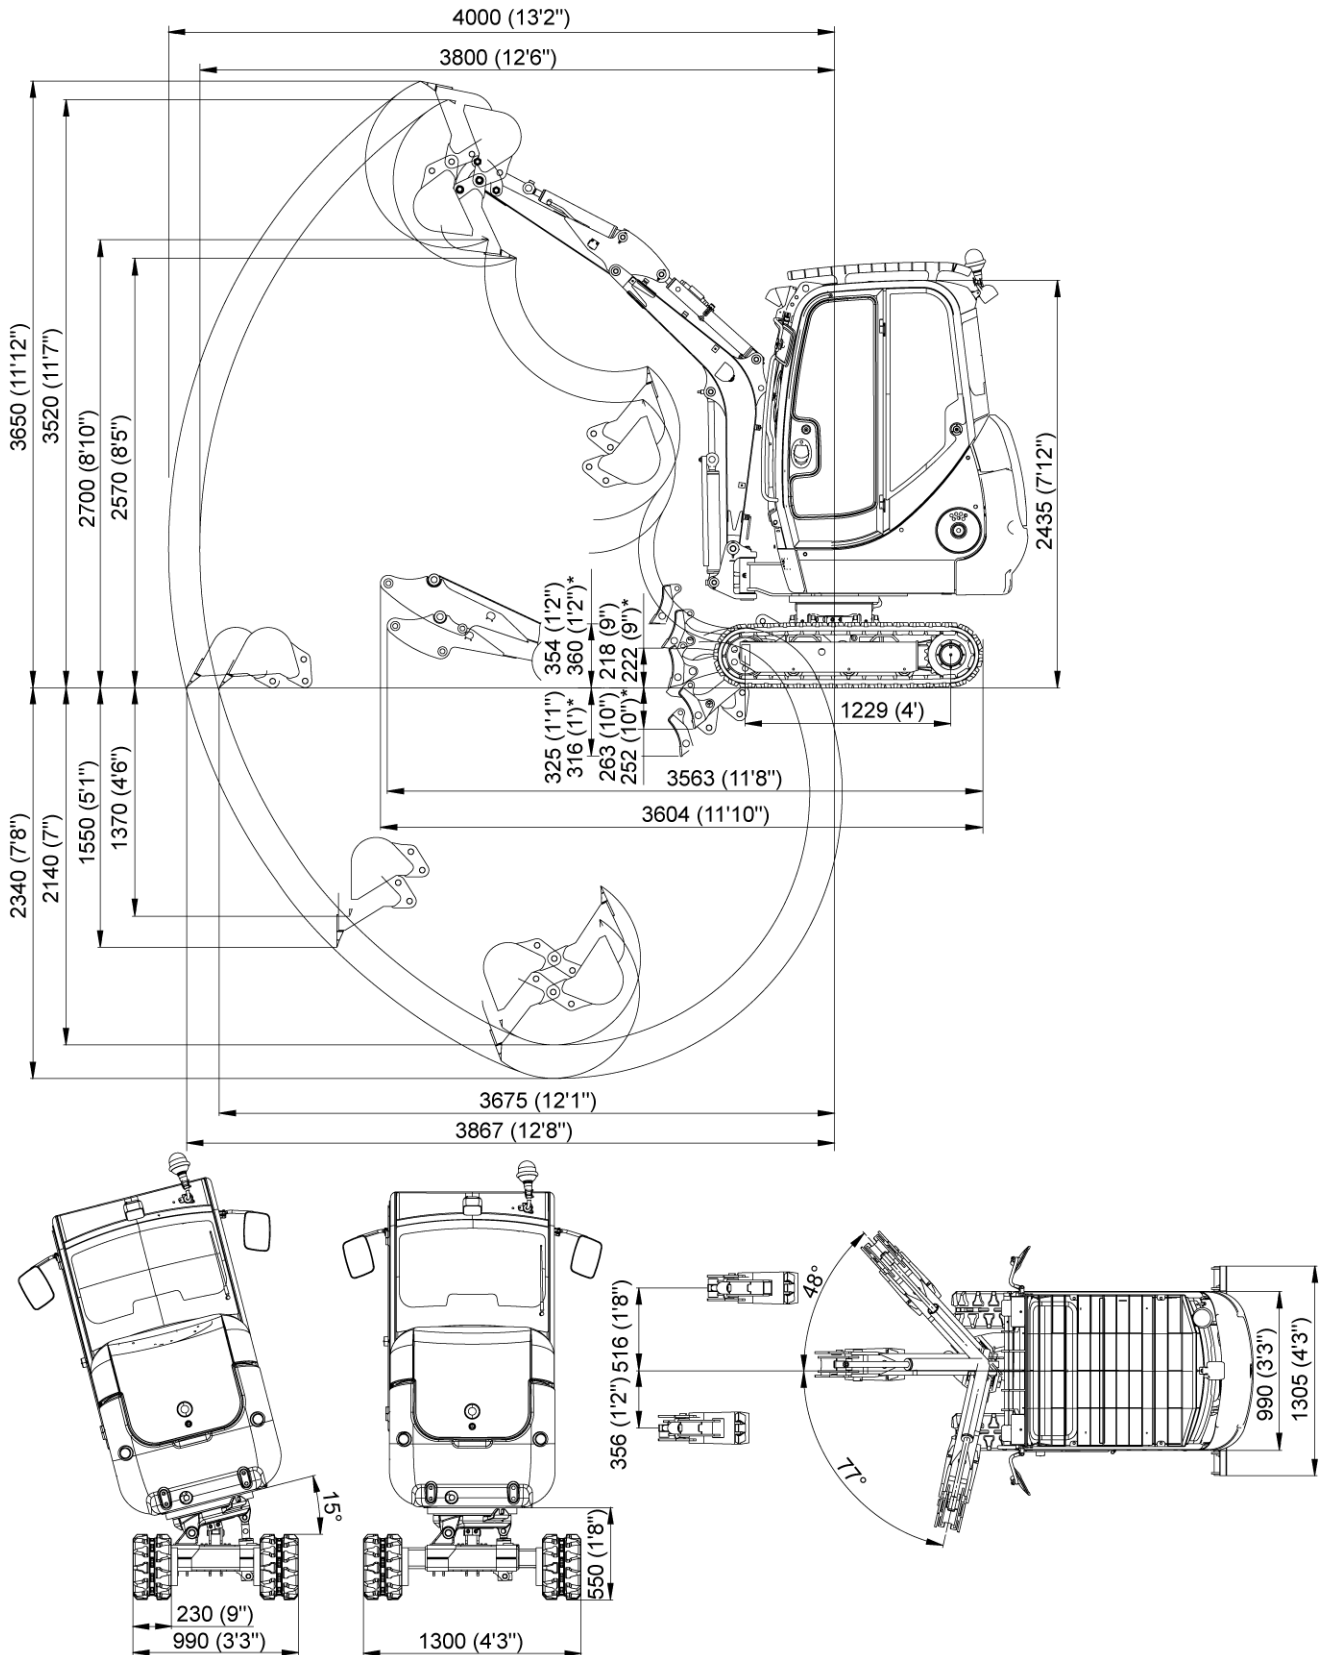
Køreøjets dimensioner (type 1703 VDS)
